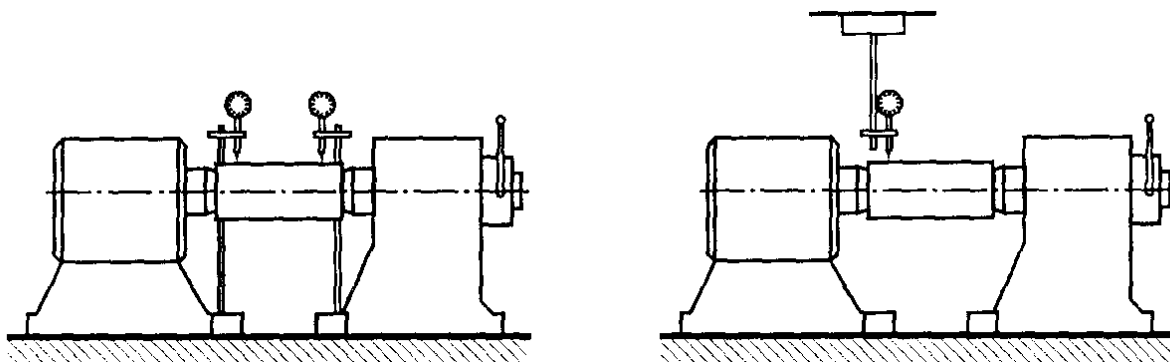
Контроль точности центров правой и левой бабок зубошвинговального станка
